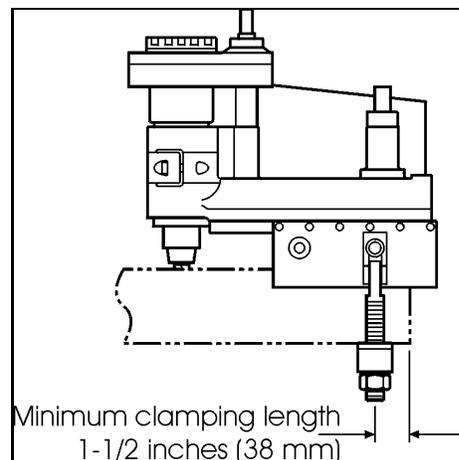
MONTAGE D'EMBOUT À COLLET
